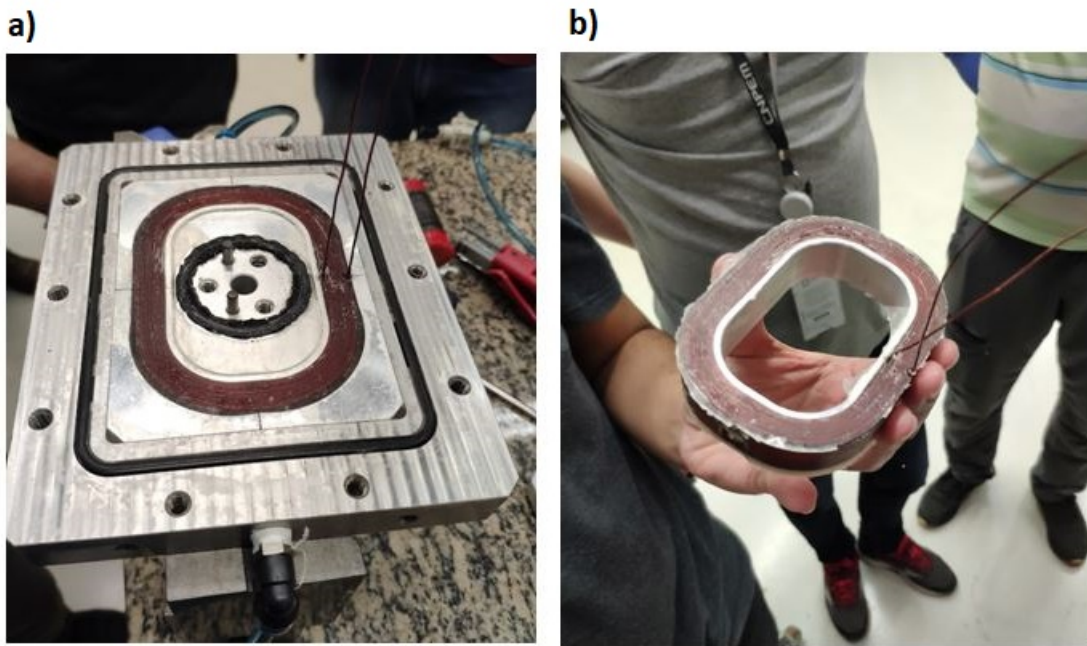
Primeiro protótipo a) durante o desmolde e b) fora do molde . Fonte: Grupo de Supercondutividade do CNPEM.
